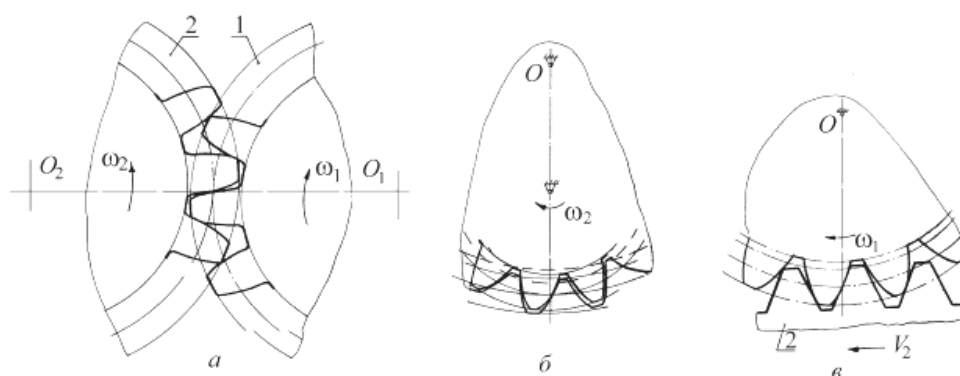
Цилиндрическая зубчатая передача: а – с внешним зацеплением; б – с внутренним зацеплением; в – реечная; 1 – ведущее звено; 2 – ведомое звено
